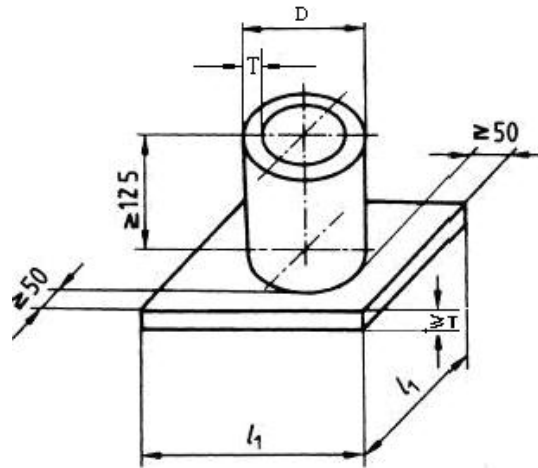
板角焊缝技能评定用试件尺寸 (单位: mm)
